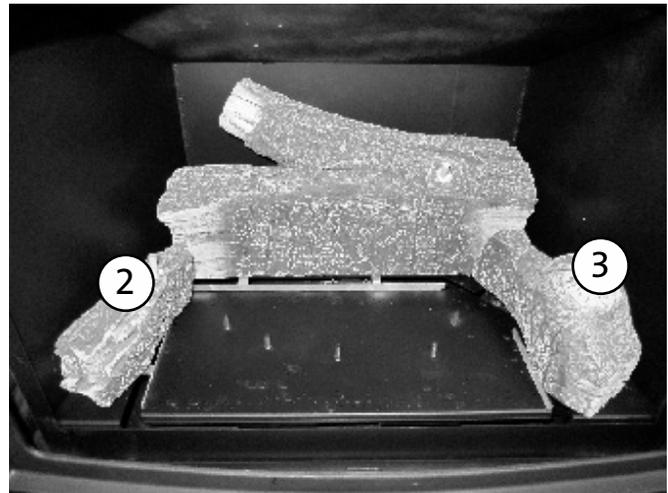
Placez les bûches avant gauche et droite sur les tiges de position au centre du plateau du brûleur.
